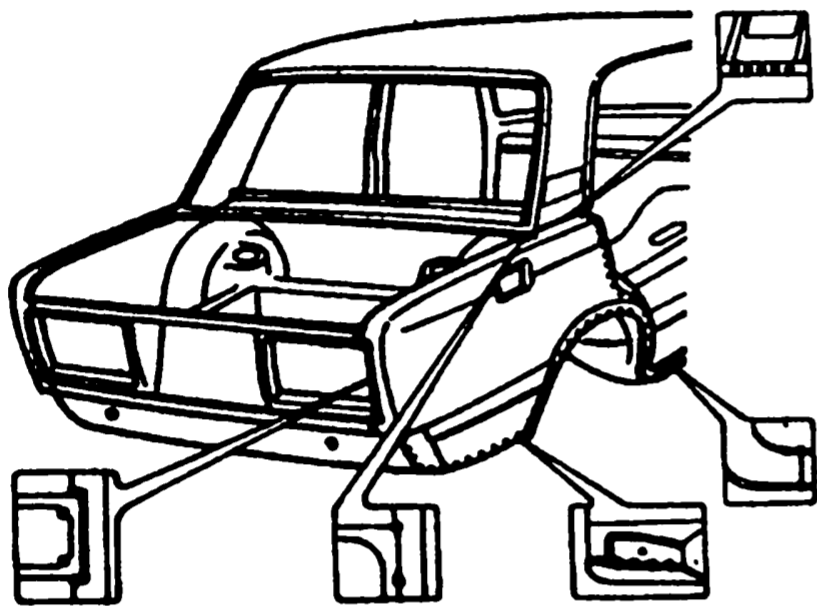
Места сварки заднего крыла. На основном виде точками обозначены швы контактной сварки. На фрагментах показаны места газовой сварки
